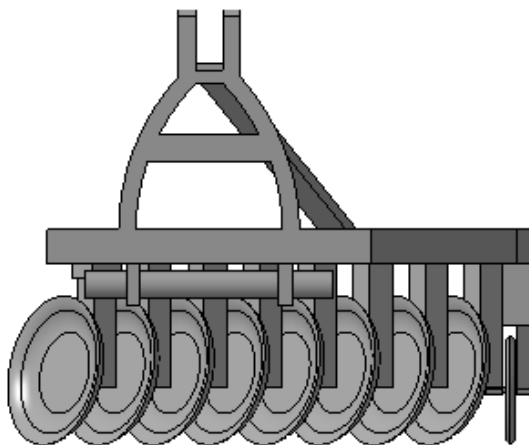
Предлагаемая конструкция плуга. Вид с переди
